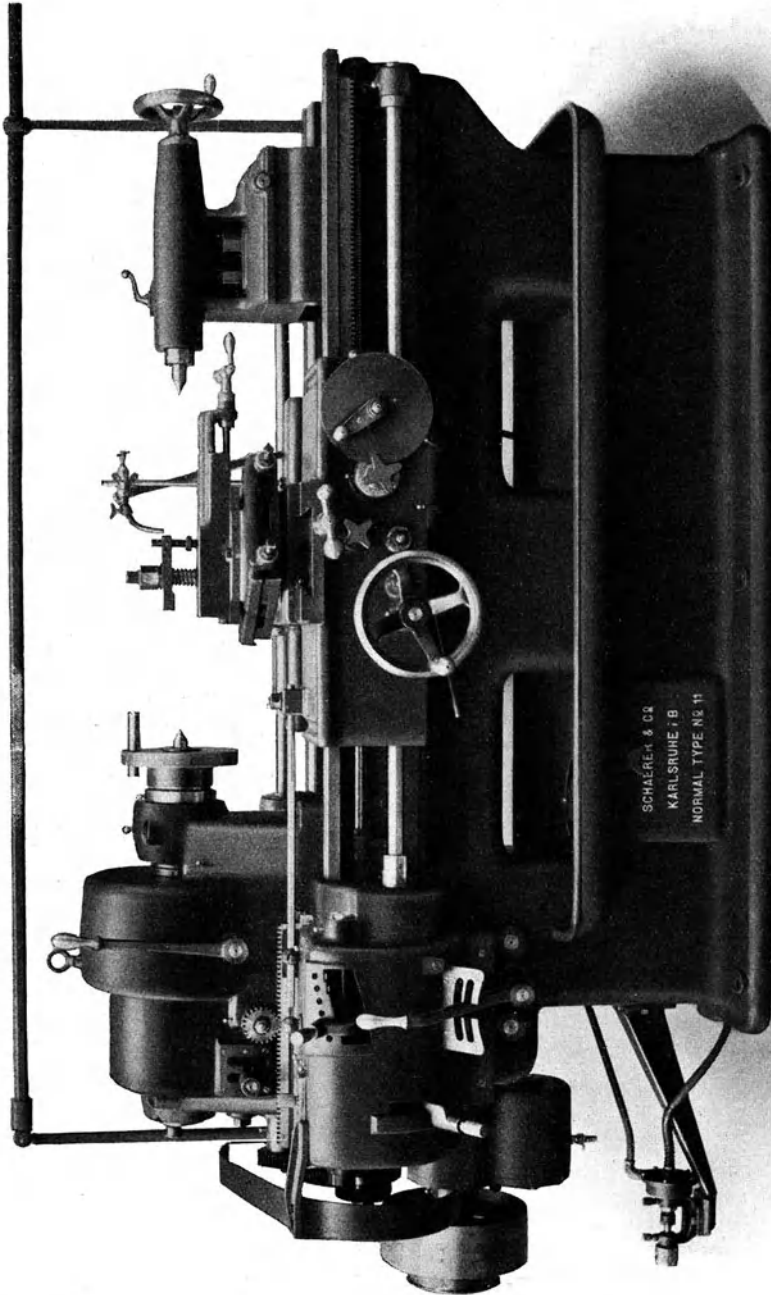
Universal-Hinterdrehbank von Schaefer & Co.
